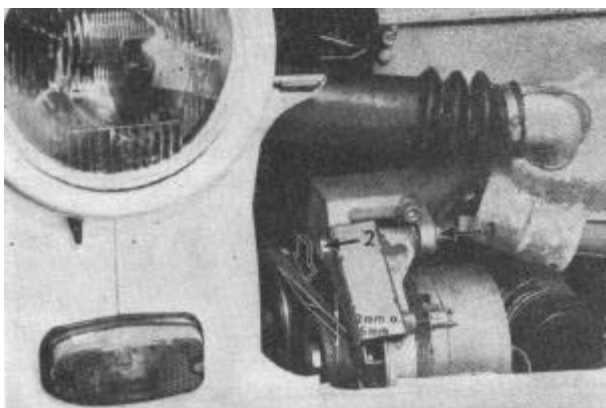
Halter der Drehstromlichtmaschine und Keilriemenspannung
